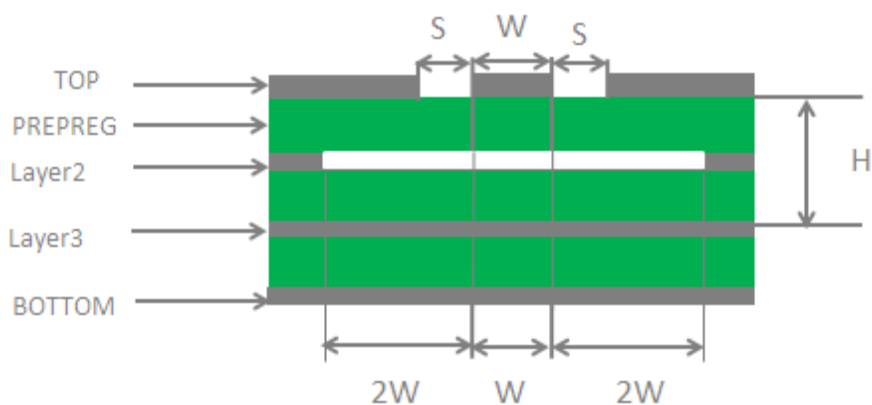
四层 PCB 板共面波导结构（参考地为第三层）
